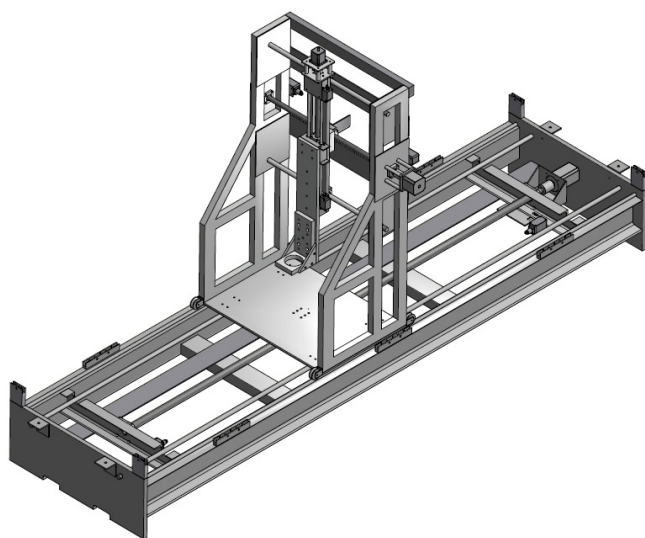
Sistema mecánico de Fresadora CNC de 3 ejes [5].
